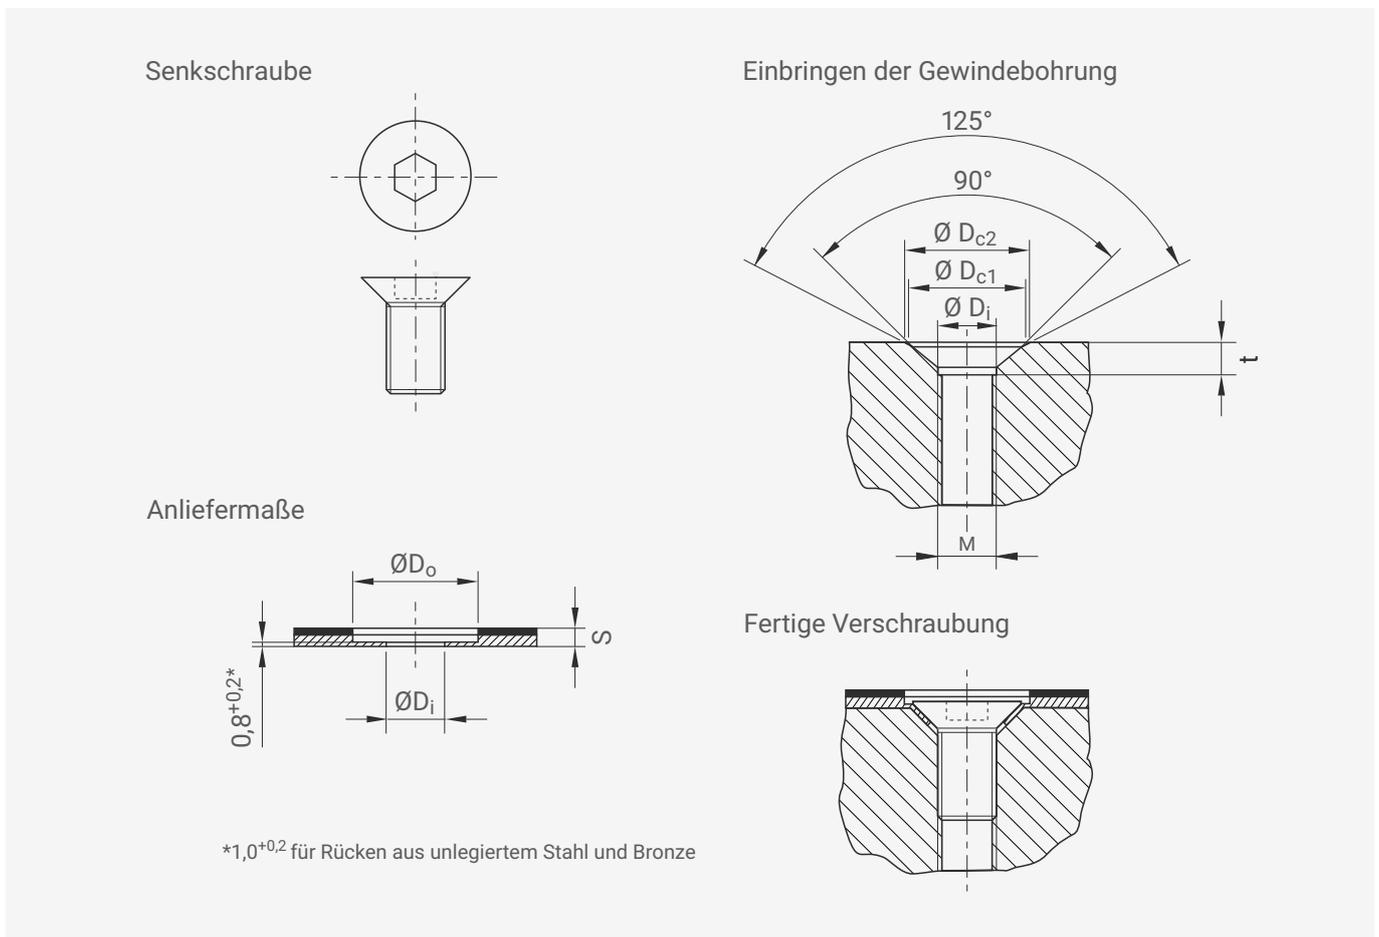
Befestigen von GGB-CBM Gleitplatten mittels Senkschrauben
